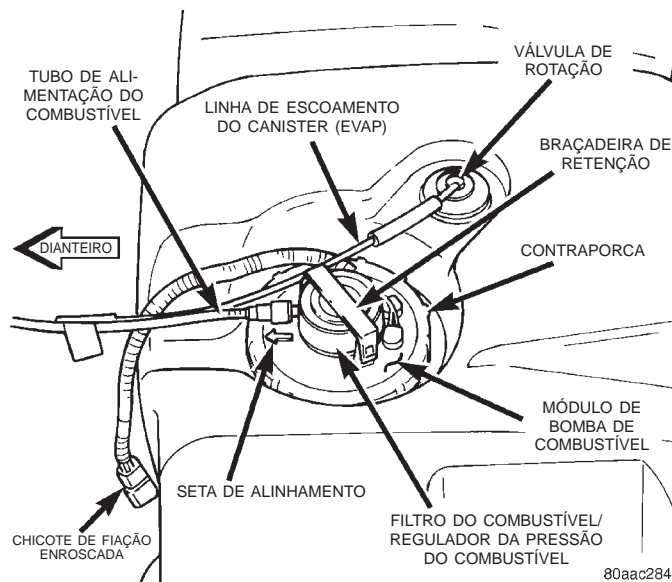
Reservatório de Combustível/Módulo de Bomba de Combustível (Vista Superior)
